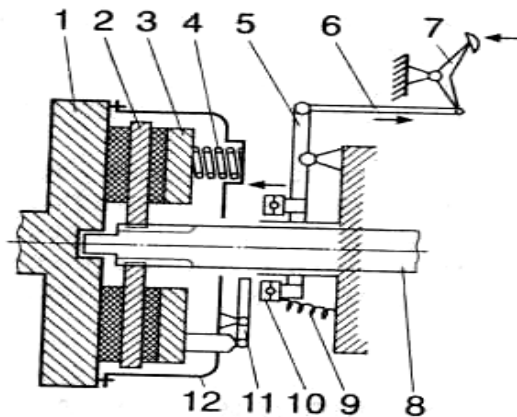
Схема фрикційного зчеплення: 1 – маховик; 2 – ведений диск; 3 – натискний диск; 4 – пружини; 5 – вилка; 6 – тяга; 7 – педаль; 8 – ведучий вал; 9 – поворотна пружина; 10 – муфта; 11 – важелі; 12 – кожух.
